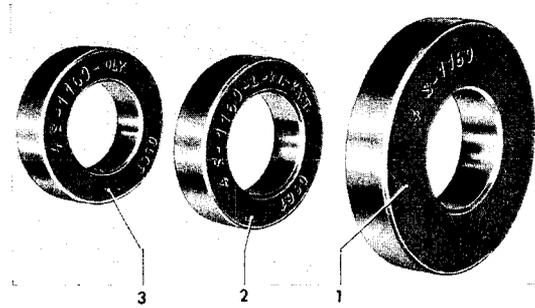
Spezial-Aufpreßringe für Hinterachswellenkugellager mit Einbauteilen
